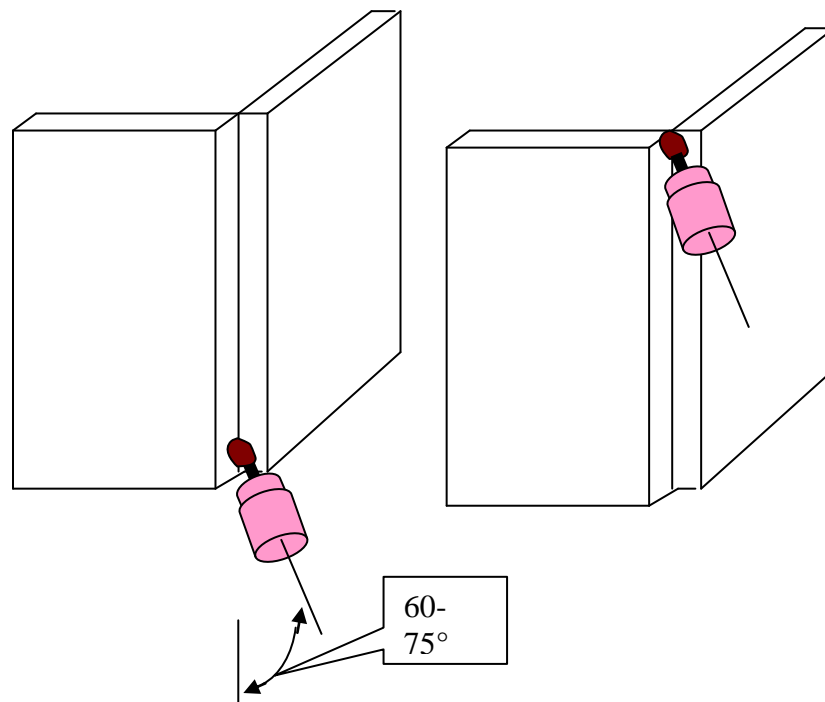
Punteado de las placas, para obtener el ensamble de soldadura en esquina, en posición vertical.
